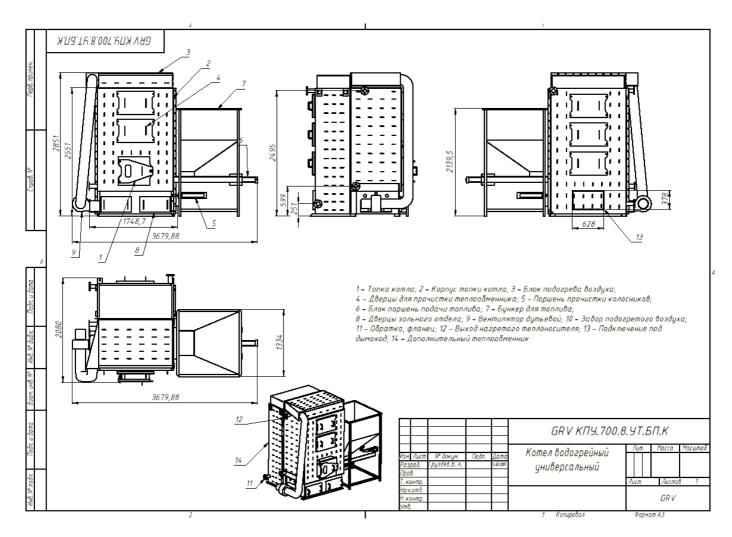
Чертеж котла. 1 — Топка котла; 2 — Корпус топки котла; 3 — Блок подогрева воздуха; 4 — Дверцы для прочистки теплообменника; 5 — Поршень прочистки колосников; 6 — Блок поршень подачи топлива; 7 — Бункер для топлива; 8 — Дверцы зольного отдела; 9 — Вентилятор дутьевой; 10 — Забор подогретого воздуха; 11 — Обратка, фланец; 12 — Выход нагретого теплоносителя; 13 — Подключение под дымоход; 14 — Дополнительный теплообменник для повышения мощности котла.
